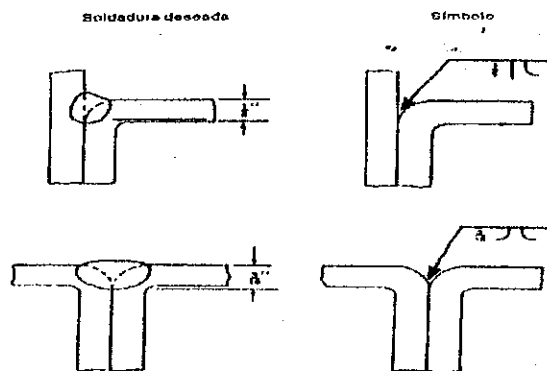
Símbolo de soldadura en el que se representa una soldadura de doble ranura de las mismas dimensiones.
